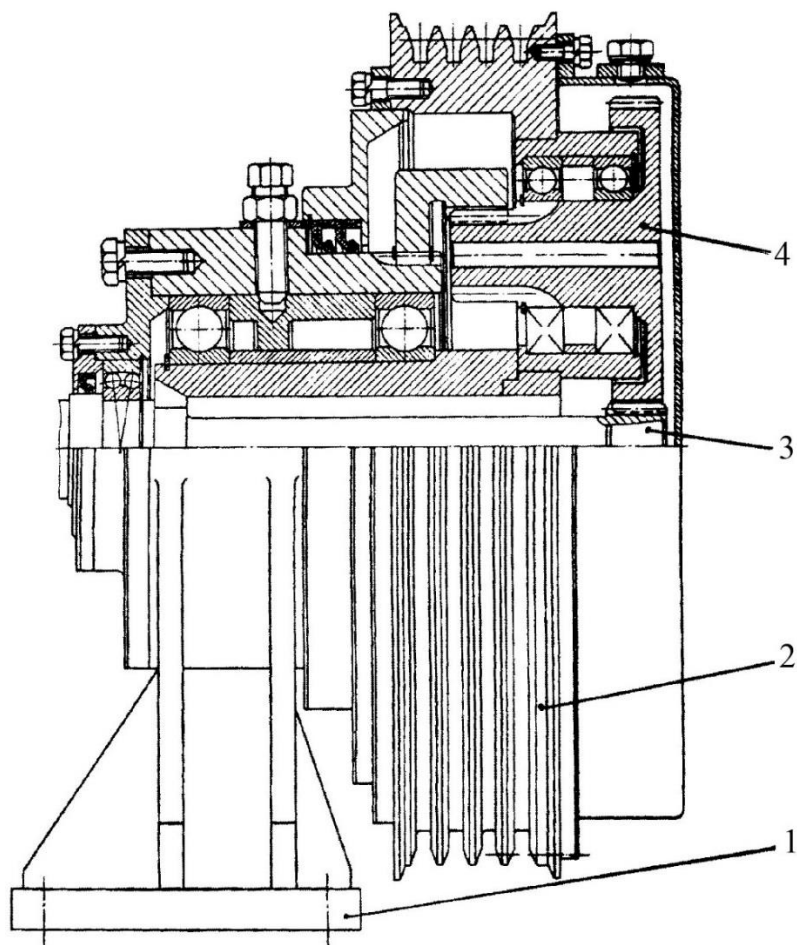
Лебедка с планетарным редуктором, встроенным в КВШ:
